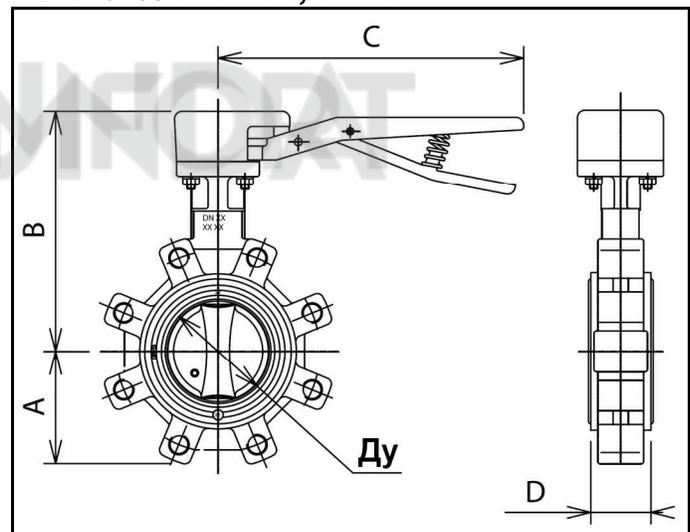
Габаритные и присоединительные размеры затворов дисковых поворотных типа VFY- LH с резьбовыми отверстиями под болты
